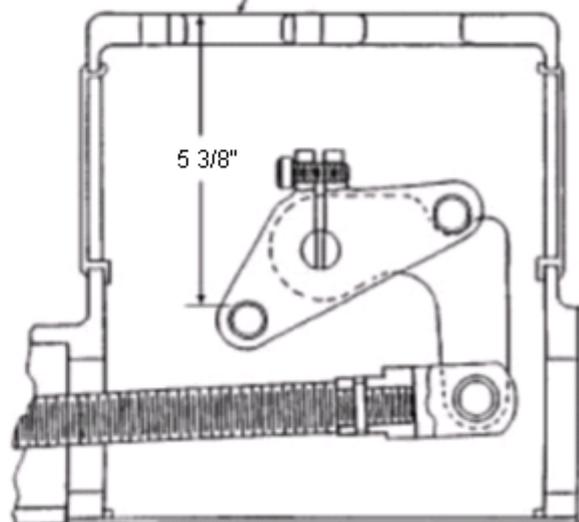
Положение рычага «воздух закрывает». Размеры В и С
